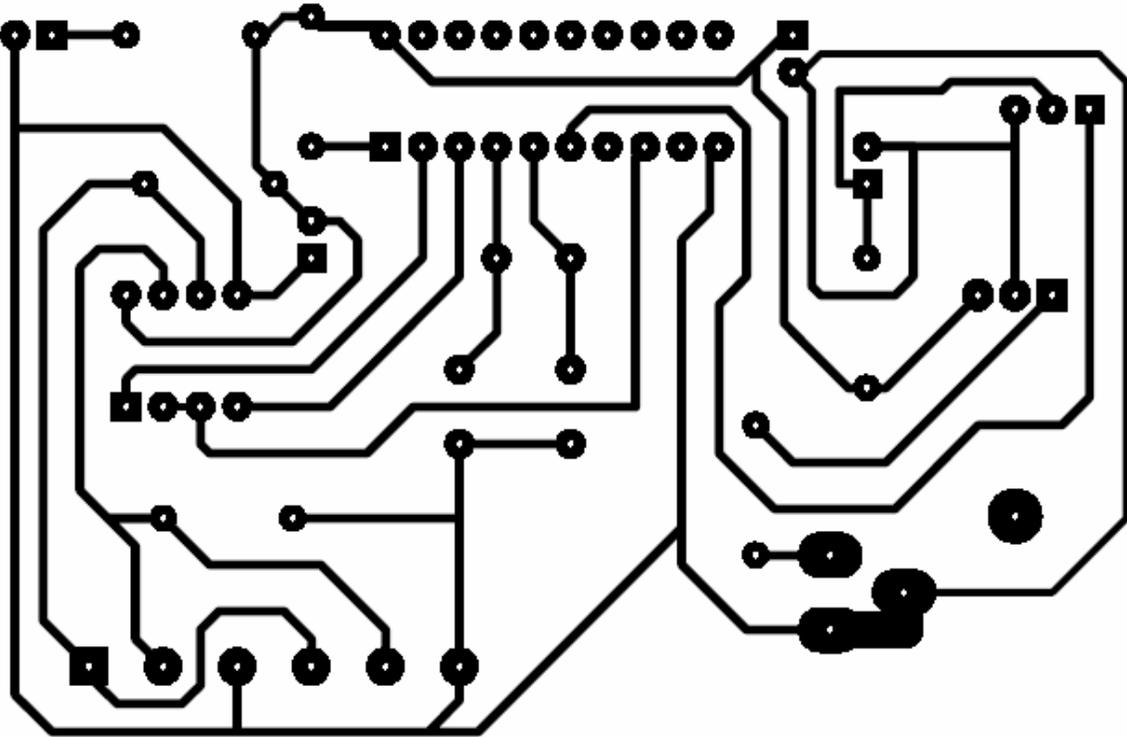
Circuito impreso del controlador central (lado de la soldadura).
